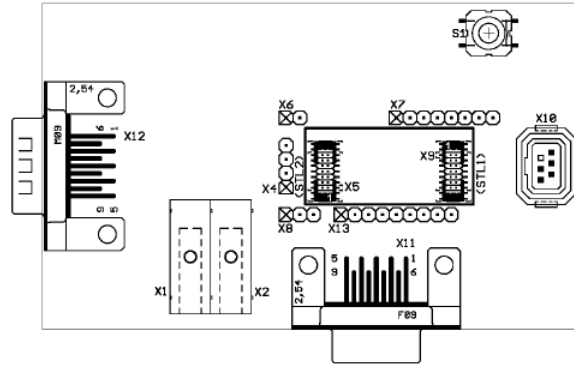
Montaje del CHipOx en la tarjeta de conexiones
